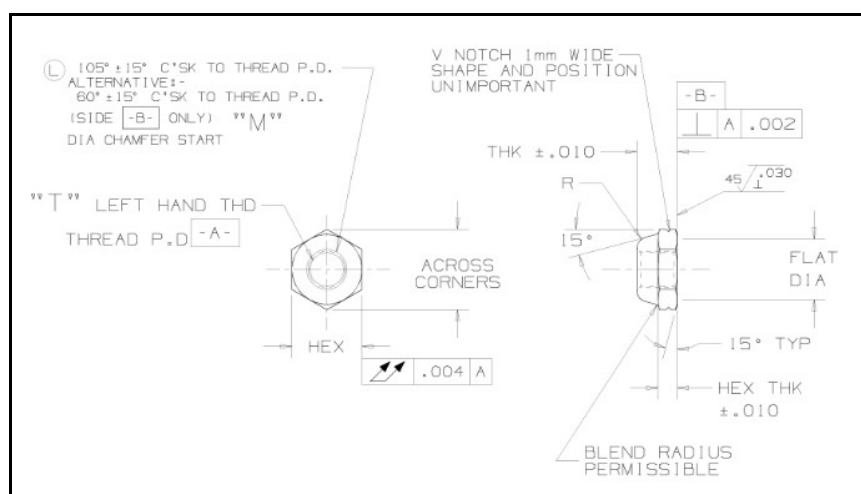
Porca instalada no eixo do rotor do turbocompressor (extraído de desenho de fabricação)
